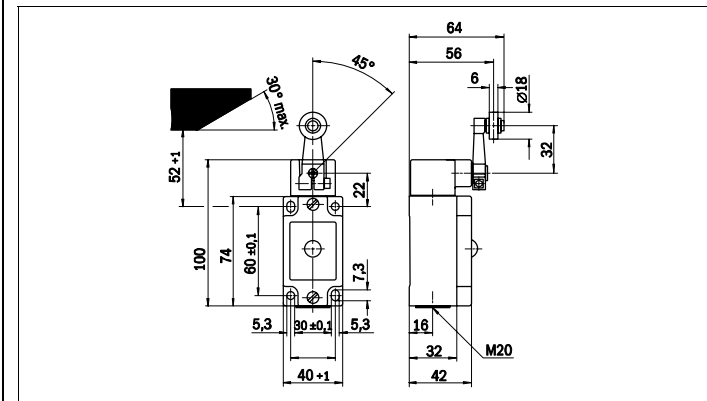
Maßbild i100R (für Schwenkhebel mit Stahlrolle)
